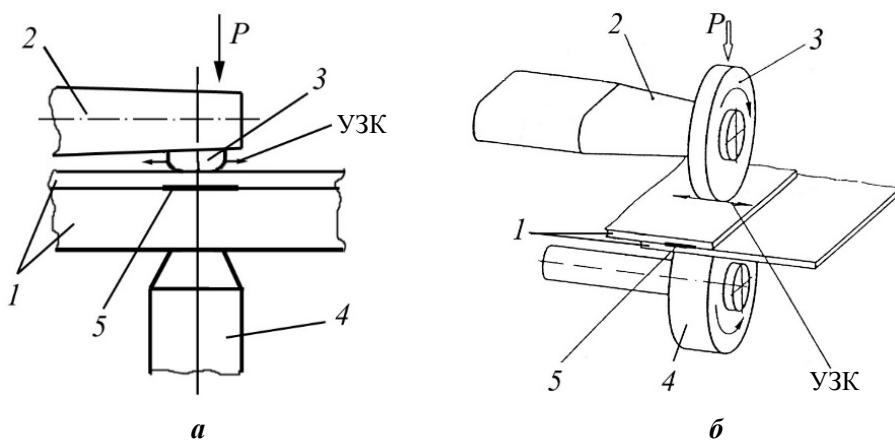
Принципова схема точкового (а) і шовного (б) зварювання ультразвуком:
